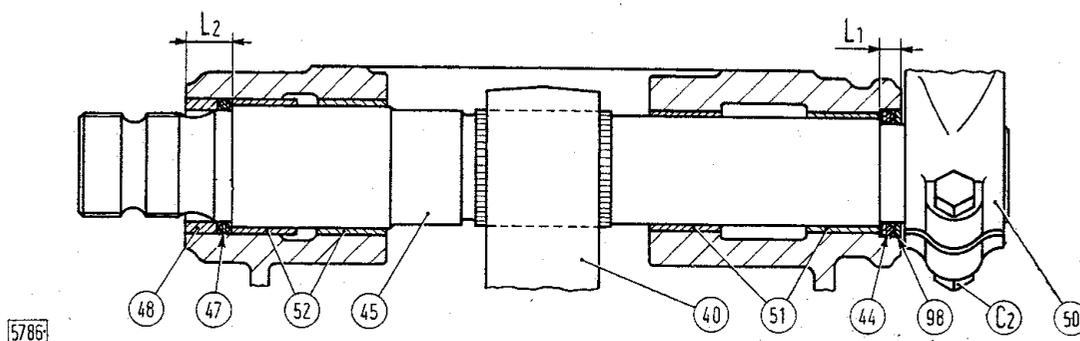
Sezione sull'albero di sollevamento bracci.
